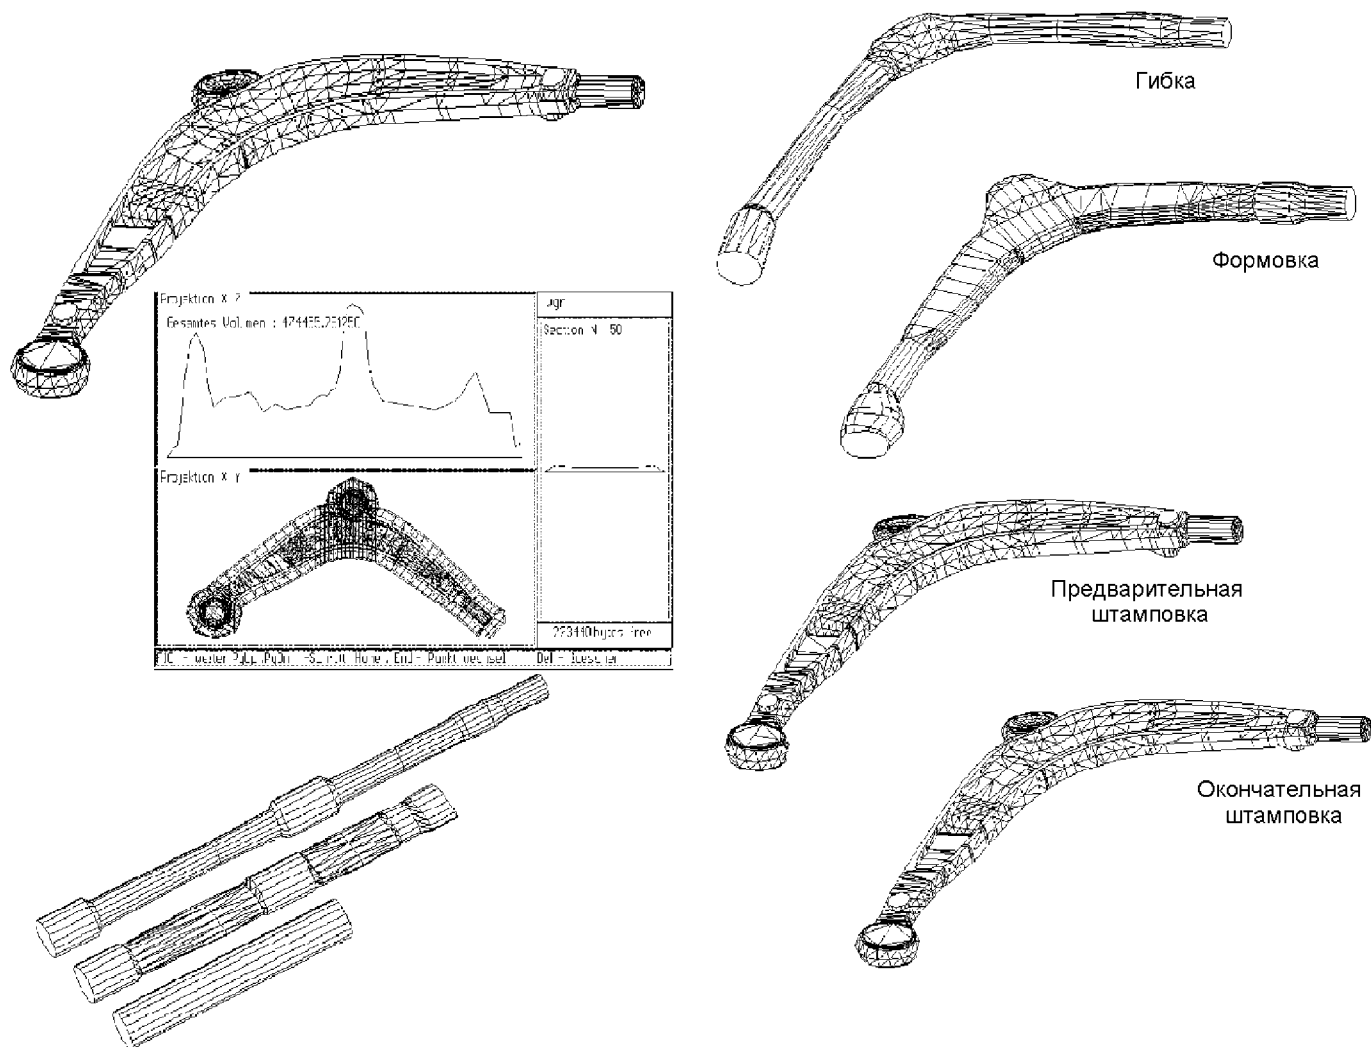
Поковка рычага передней подвески, эпюра площадей сечений поковки с облоем и переходы профилирования заготовки на ковочных вальцах.
